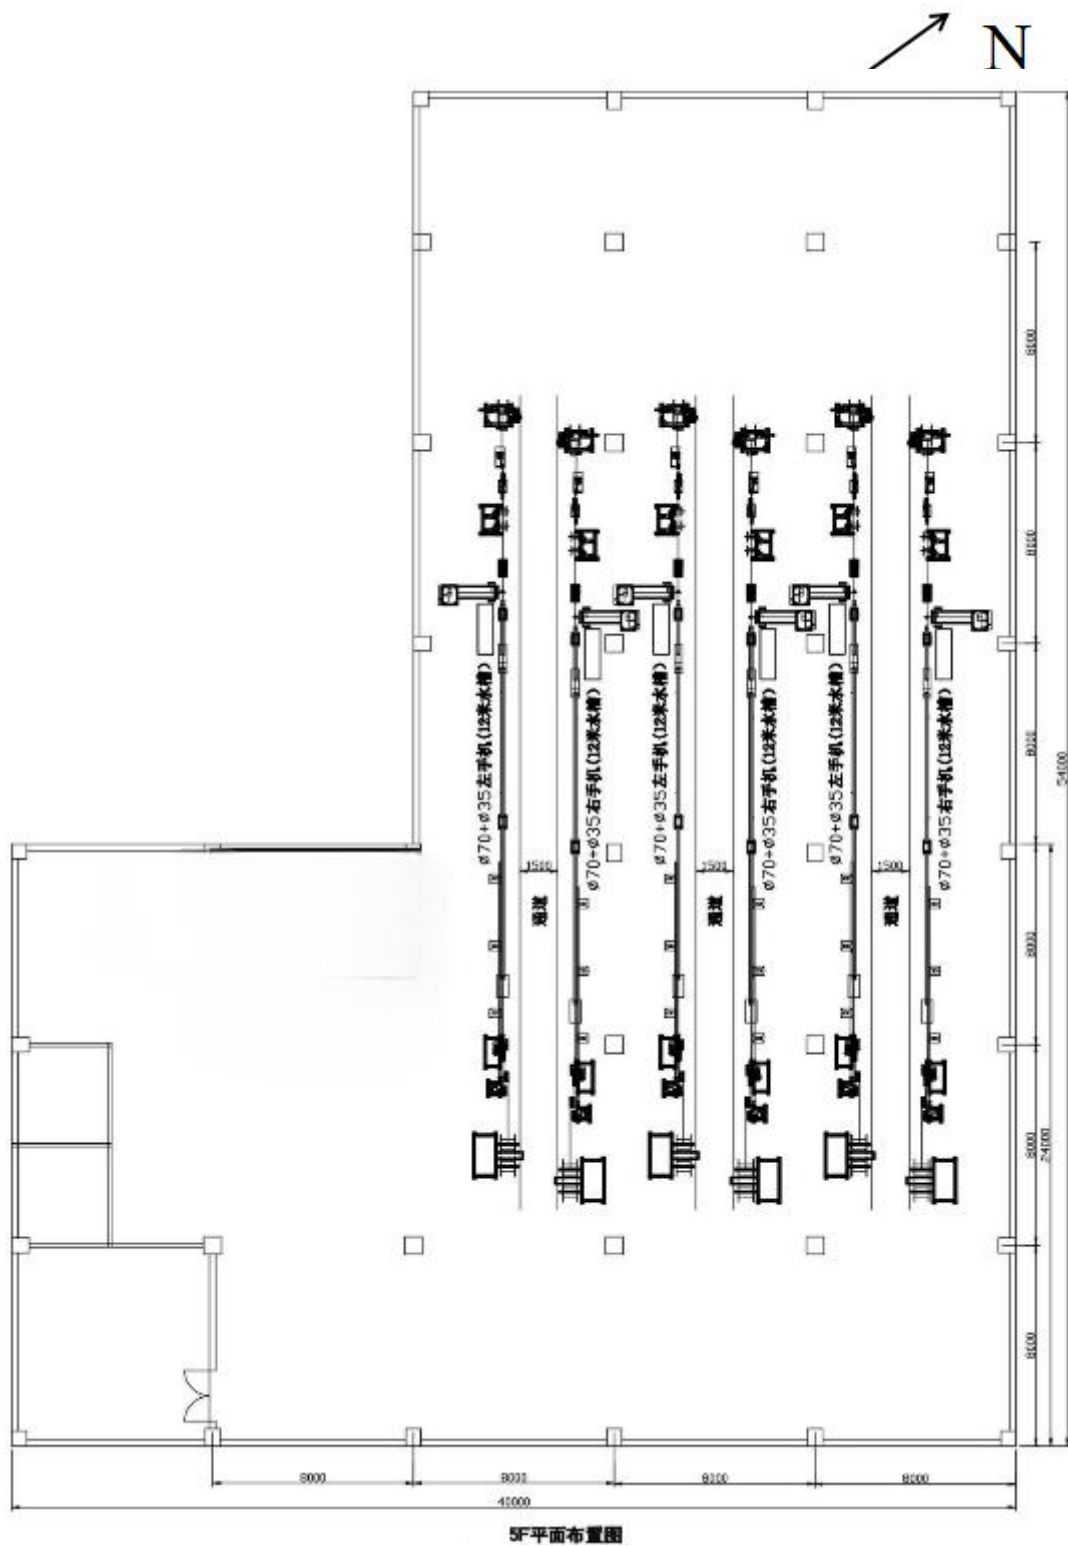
车间平面布置图（5 栋和 6 栋的 5 楼）
